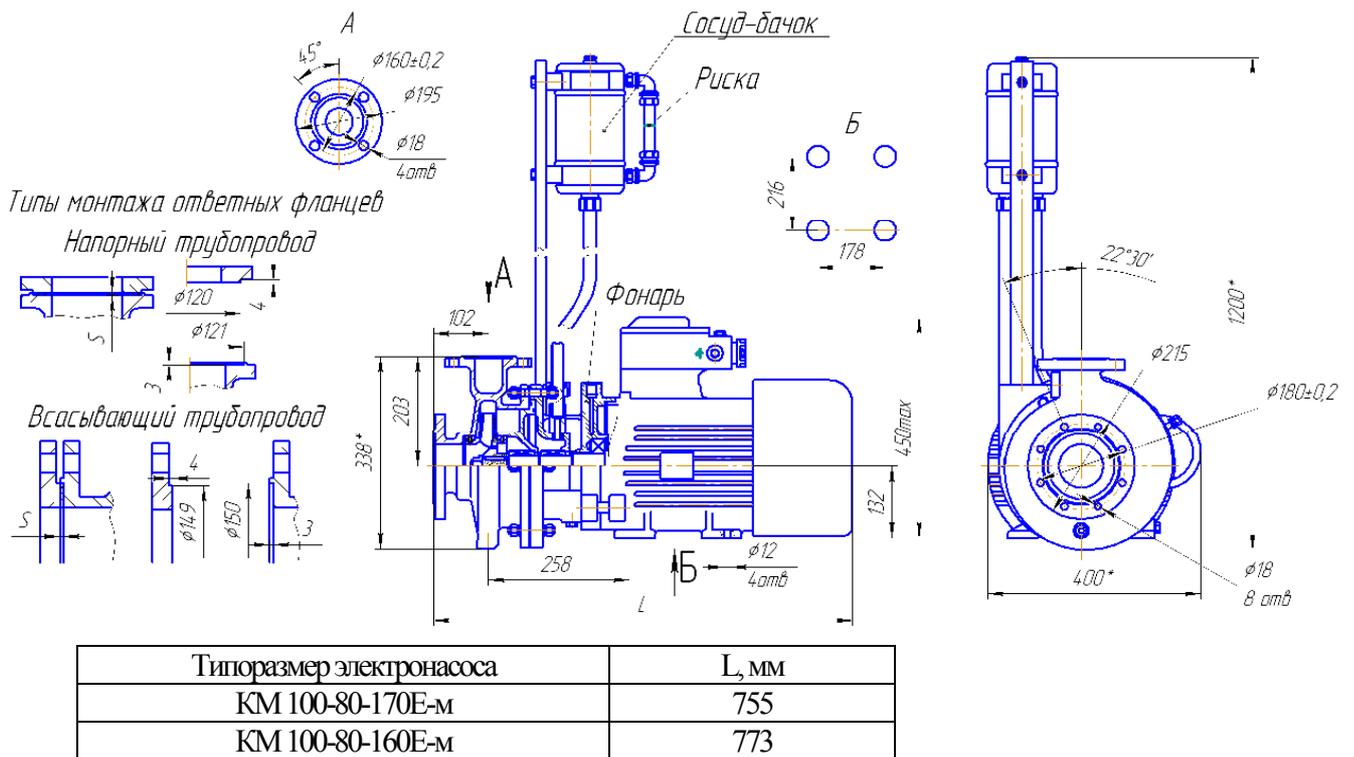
Габаритные и присоединительные размеры KM 100-80-170E-м, KM 100-80-160E-м с двойным торцовым уплотнением
